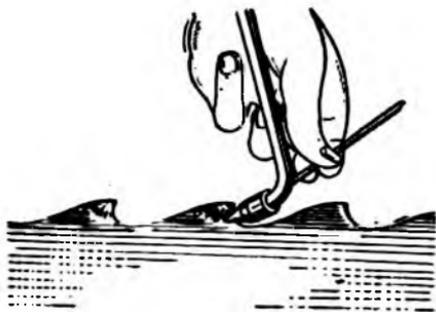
Наплавка стеллита на зуб ленточной пилы
